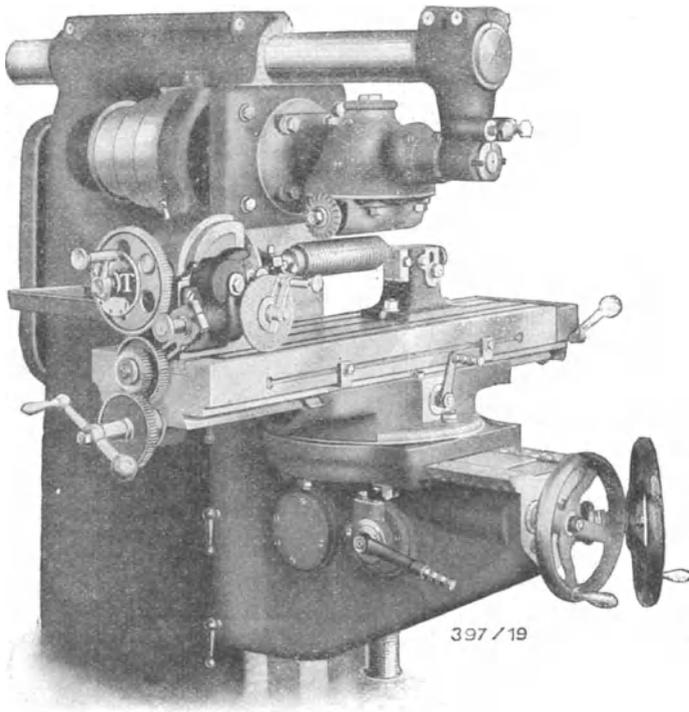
Wanderer Universalfräsmaschine mit Fräserkopf zum Gewindefräsen.
